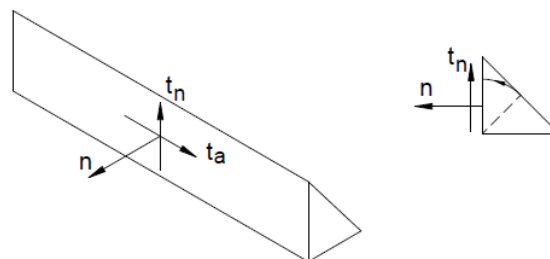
Esfuerzos en el cordón de soldadura
